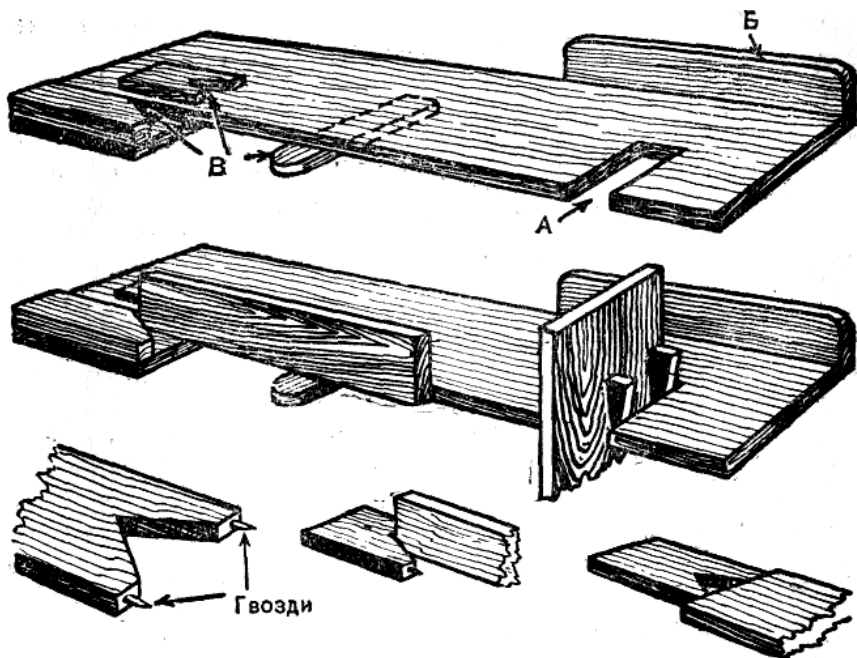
Крышка рабочего стола упрощенной конструкции:
